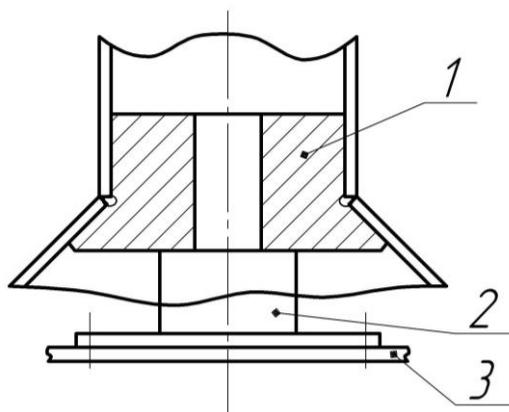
Схема приспособления: 1 – центрирующая шайба; 2 – стойка; 3 – планшайба манипулятора
